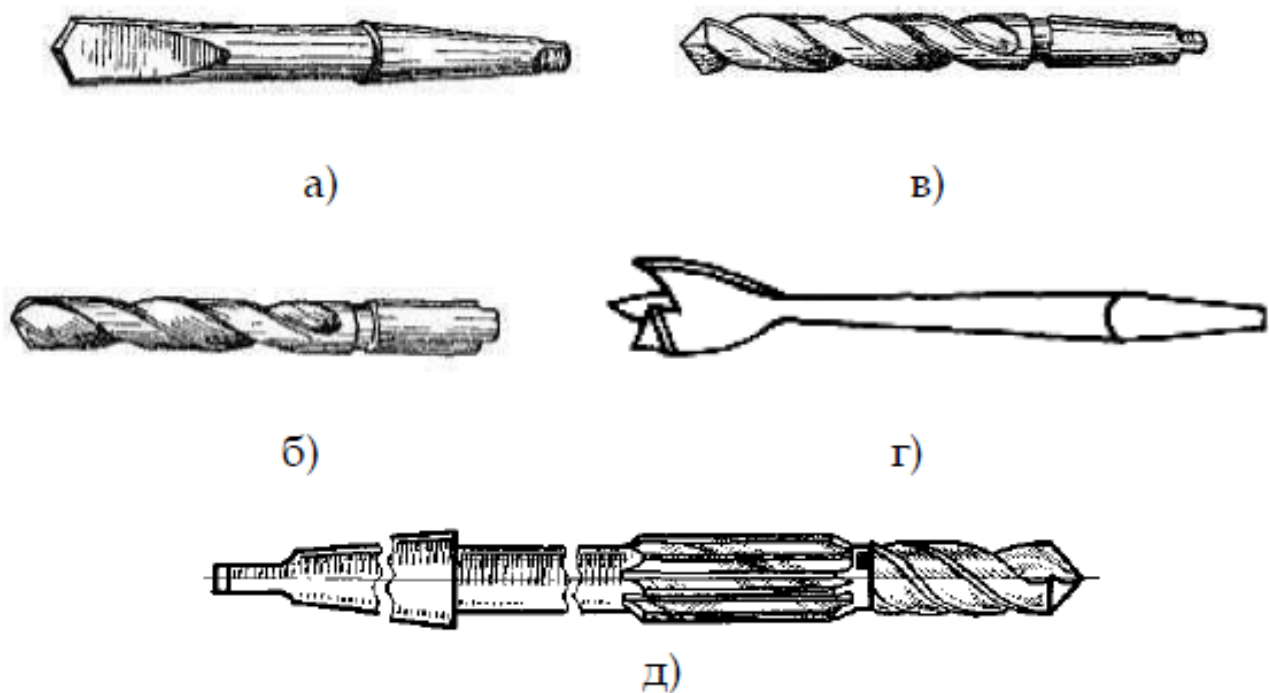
Свердла а – перові; б, в – спіральні; г – центрові; д –
